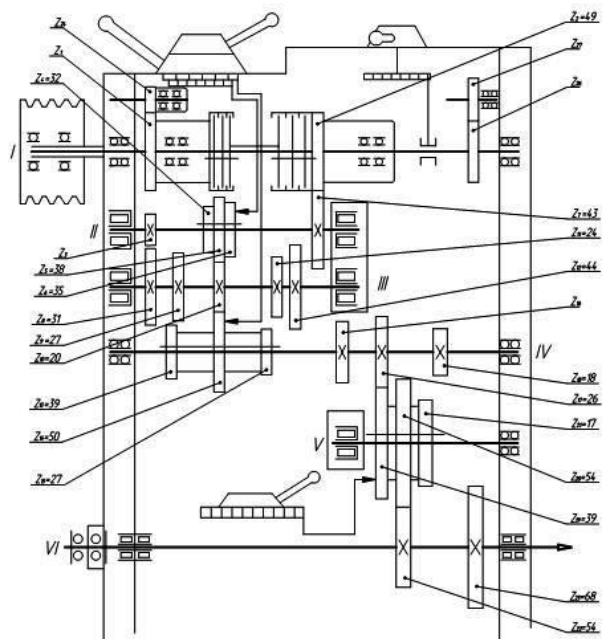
Кинематическая схема коробки скоростей привода главного движения токарного станка SN-401
